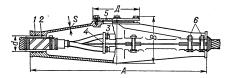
Чугунная соединительная муфта на напряжение до 1 кв: 1— корпус; 2— подмотка смоляной ленты; 3— соединительная гильза; 4 — фарфоровая распорка; 5 — крышка; 6 — крепёжные болты; A, B, \mathcal{A} , S, d — размеры, определяющие габариты муфты.
